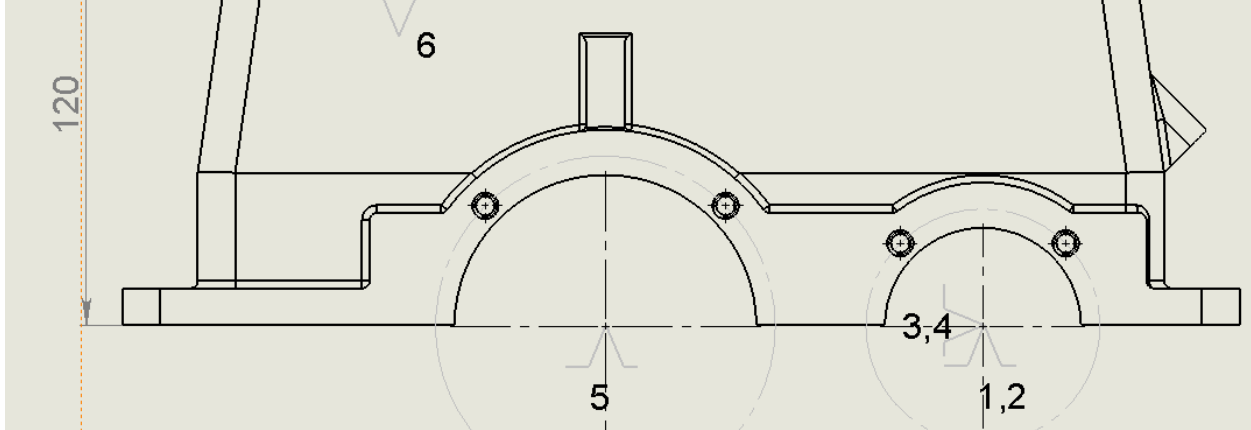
Схема установки корпуса редуктора для обработки установочной поверхности корпуса 120H8  $(+0,063)$
